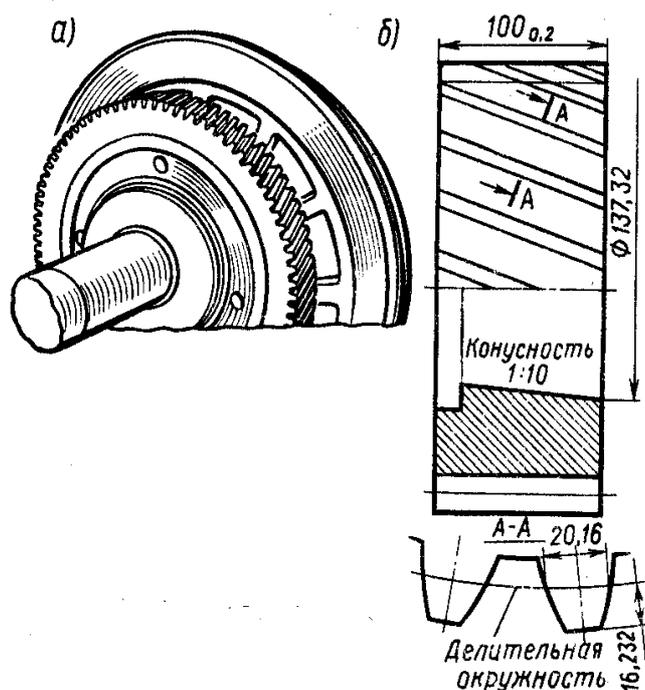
Зубчатое колесо (а) и шестерня (б) косозубой передачи
